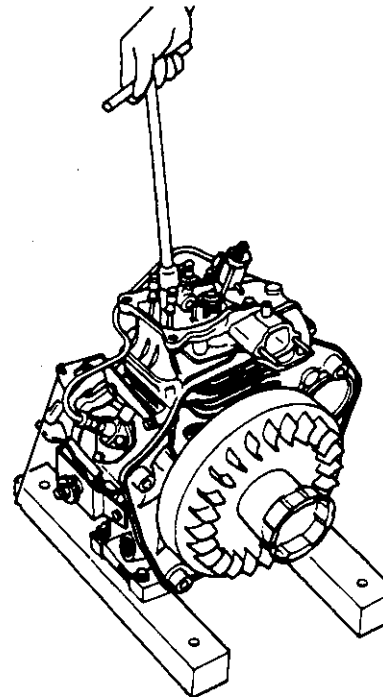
Remoção do conjunto do braço do balancim da válvula
